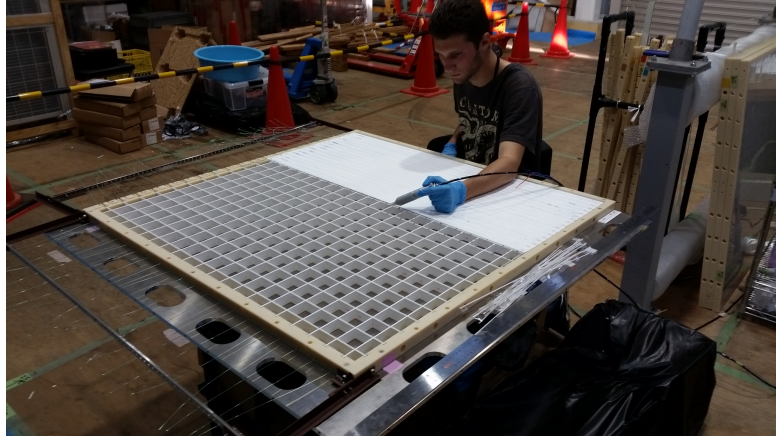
Assemblage et collage d’un plan de scintillateurs recouvrant une grille.
